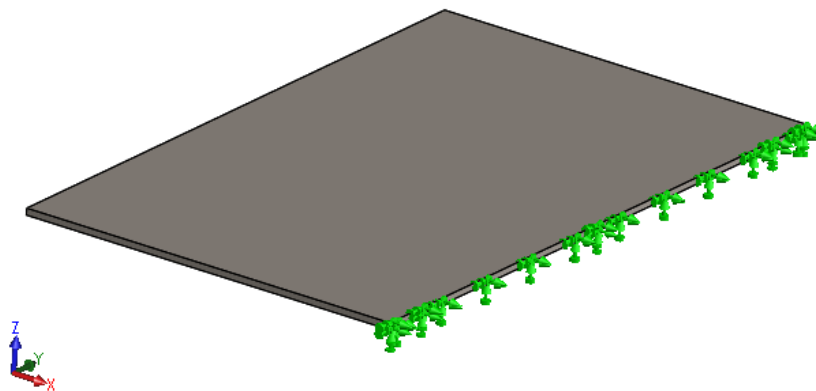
Plancha en voladizo con sujeción fija en el extremo.
